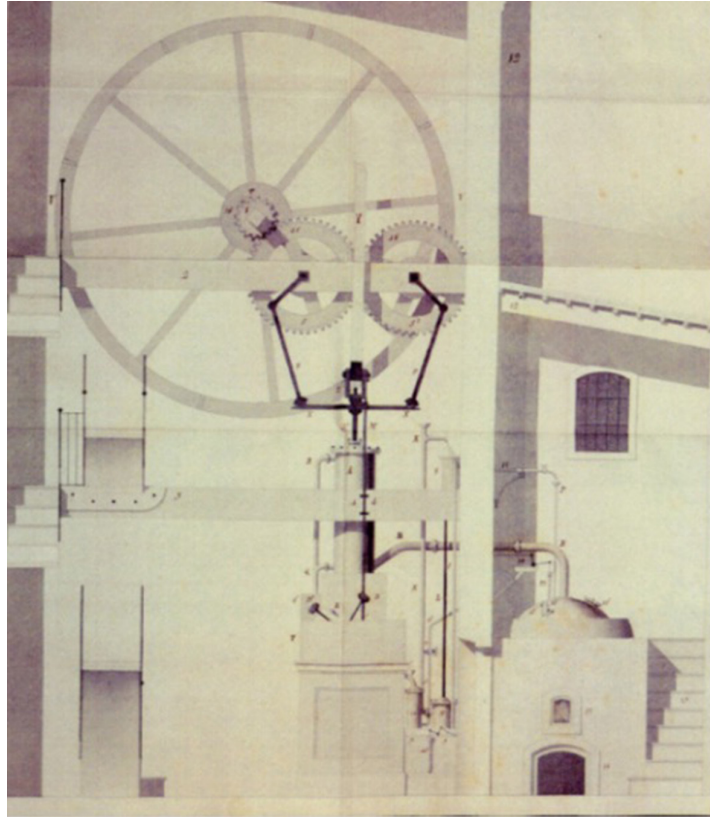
Plànol complet de la màquina realitzat per Santponç on es veuen els engranatges, el pinyó i el volant d'inèrcia.
